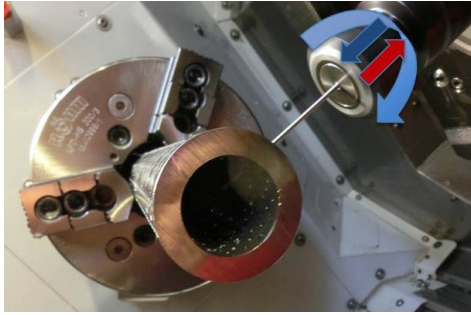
Versuchsablauf mit dem Burr-Off-Werkzeug
